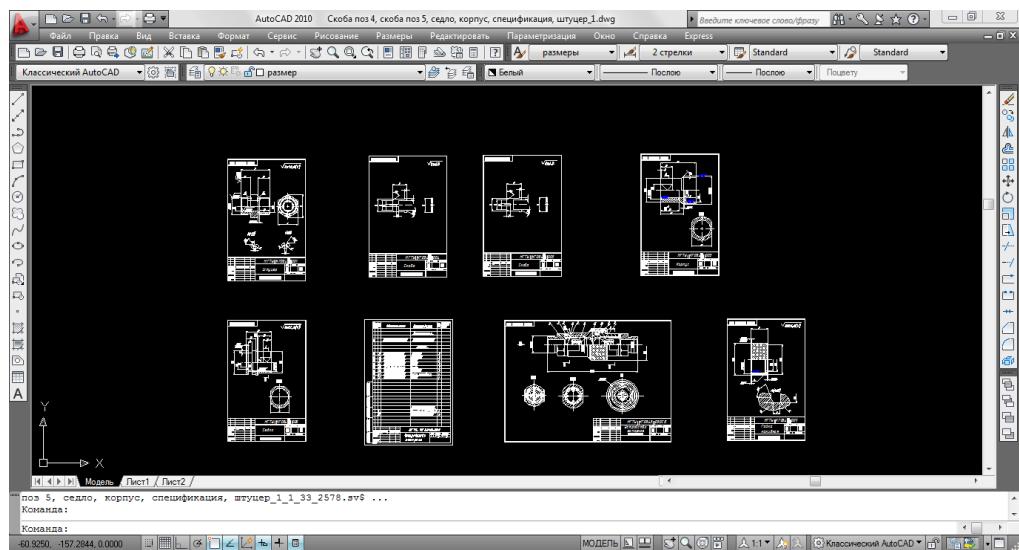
Рабочие и сборочный чертежи запорного клапана
